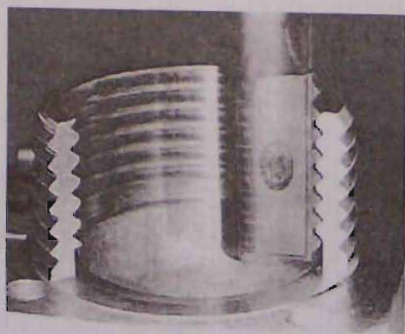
Osmiosé centrum Avant fy P.Bacci z Casciny u Pisy [20]
